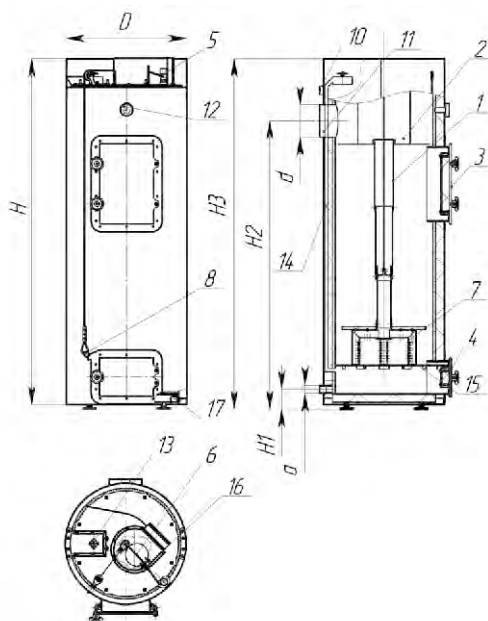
Габаритные и присоединительные размеры универсальной версии Comfort-XXG (1 – телескопическая труба подачи воздуха, 2 – камера подогрева воздуха, 3 – проем для загрузки дров, 4 – проем для удаления золы, 5 – терморегулятор, 6 – устройство для регулирования подачи воздуха, 7 – распределитель воздуха, 8 – трос, 10 – патрубок подачи воды, 11 – дымоход для отвода дымовых газов, 12 – термоманометр, 13 – регулятор подачи воздуха под колосниковую решётку, 14 – воздуховод, 15 – колосниковая решётка, 16 – воздушный короб с вентилятором).
